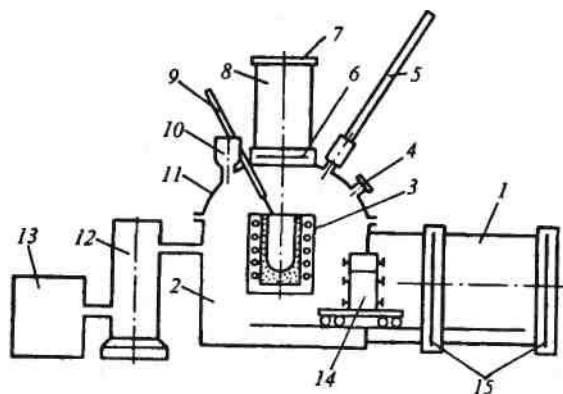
Схема вакуумной индукционной печи полунепрерывного действия: 1 - камера изложниц; 2 - плавильная камера; 3 - индуктор с тиглем; 4 - гляделка; 5 - термопара; 6 - затвор; 7 - крышка; 8 - шлюзовая камера; 9 - ломик для осаждения шихты; 10 - шлюзовой дозатор; 11 - съемная крышка; 12 - бустерные насосы; 13 - форвакуумные насосы; 14 - изложницы; 15 - задвижки
